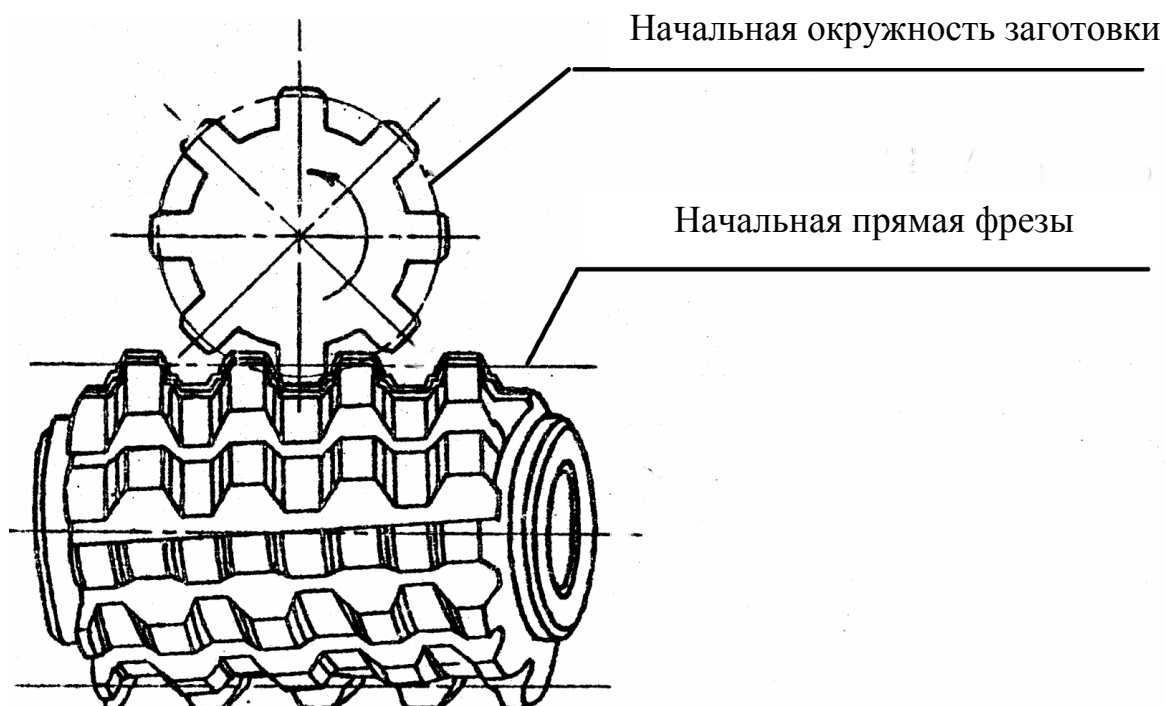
Схема нарезания шлицев червячной шлицевой фрезой
